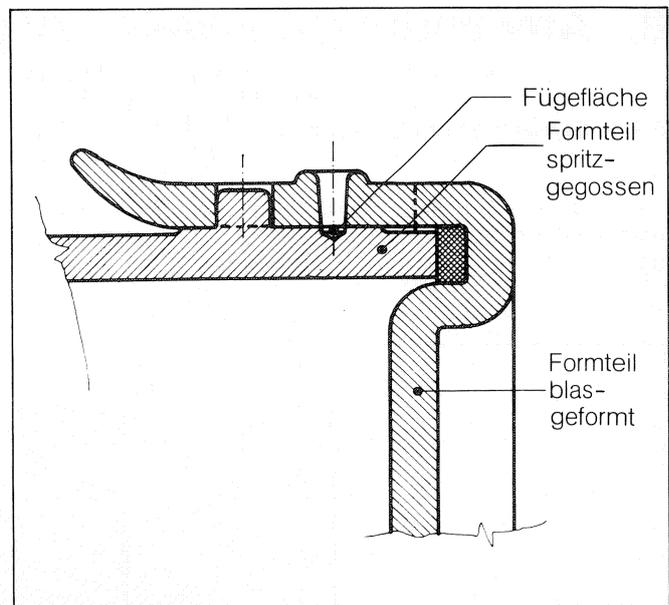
Ultraschall-Punktschweißen von blasgeformten mit spritzgegossenen Formteilen
